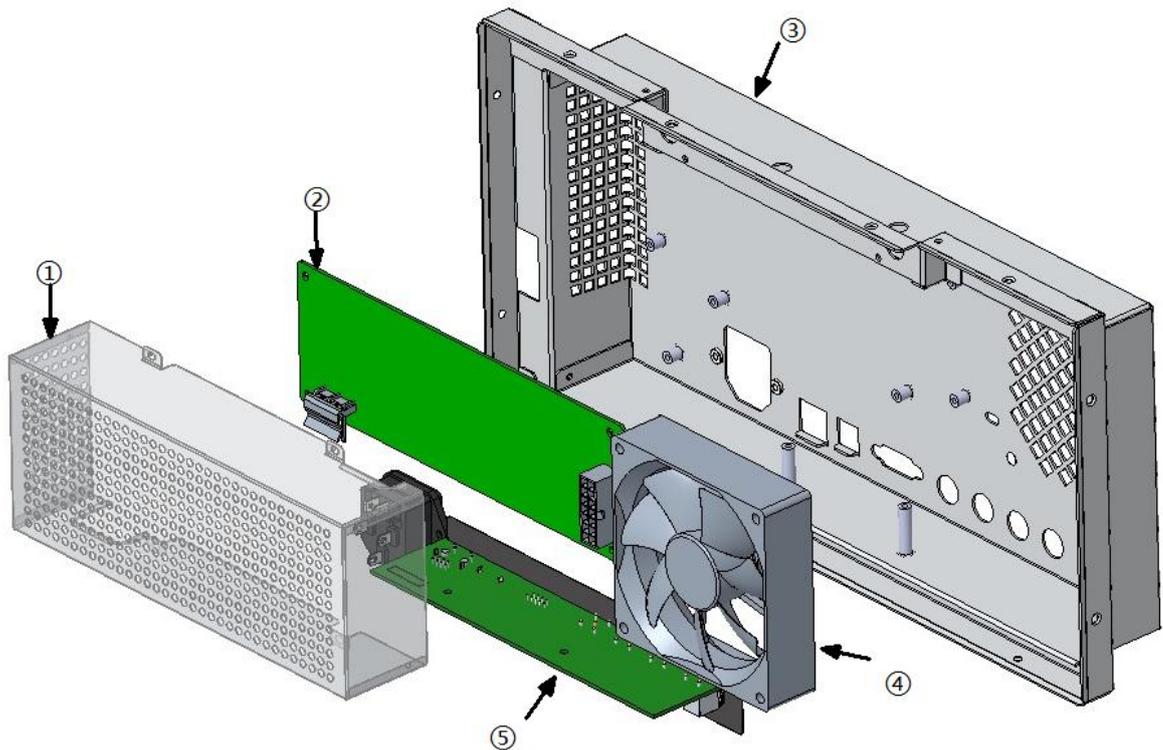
Hintere Gehäusebaugruppe mit Netzteil und Lüfter – Explosionszeichnung
